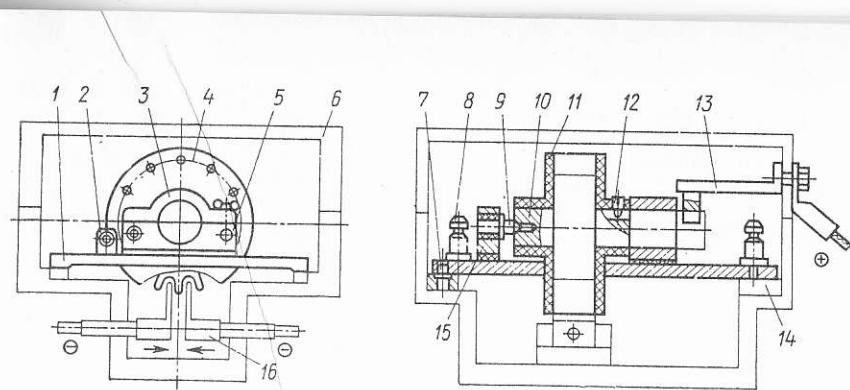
Приспособление-спутник для ЭХО лопаток монолитного ротора
